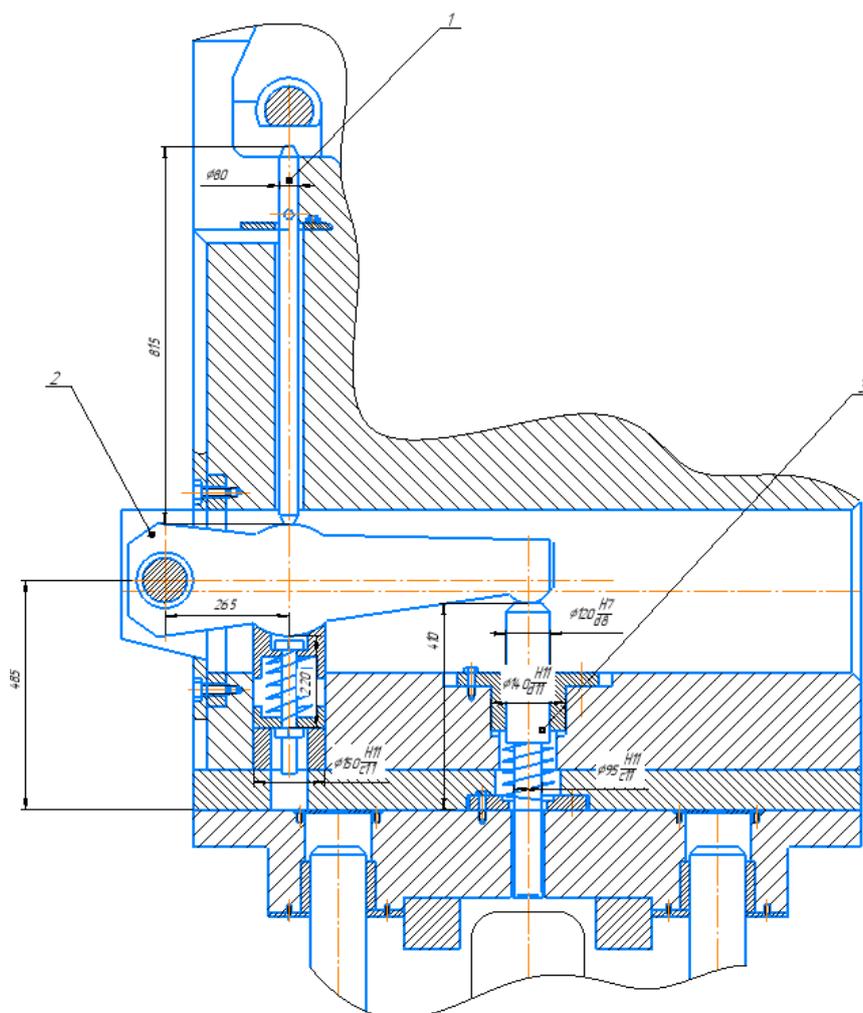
Схема механизма выталкивателя для расчета массы деталей
